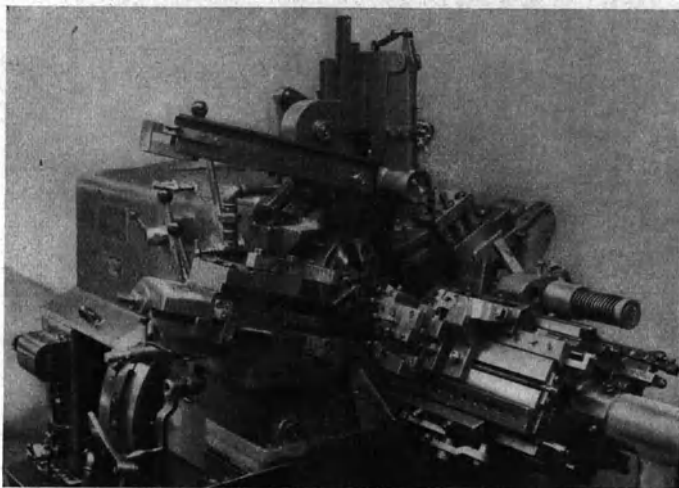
Ansicht einer Werkzeugeinrichtung für ein Arbeitsstück, das durch Magazin auf dem oberen Seitenschlitten zugeführt wird.
